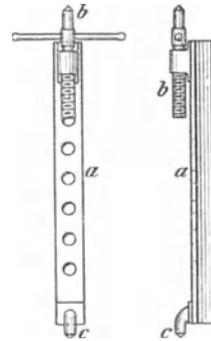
Einseitiges, gekröpftes Gestell für Handbohrmaschinen.
